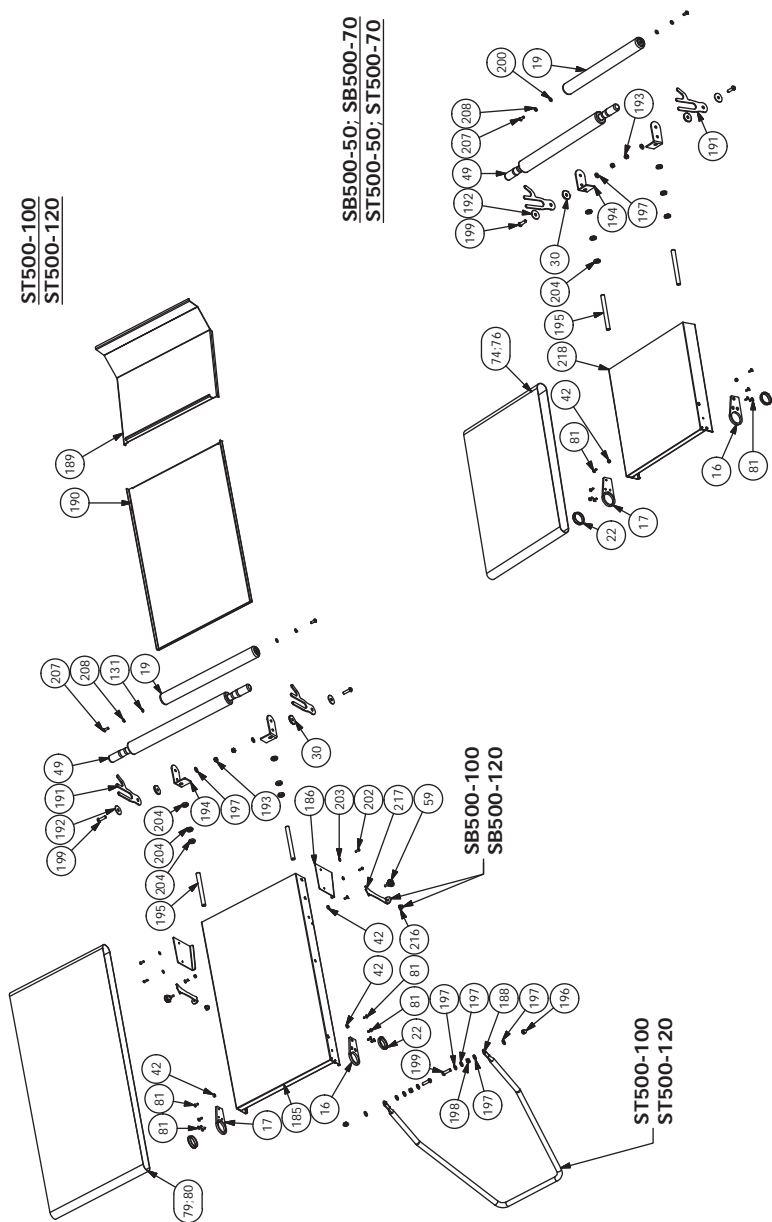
FIG. / ABB. / PИC. 21 - SB500-ST500 Parti di ricambio / Spare parts / Pieces de rechange / Repuestos / Ersatzteile / Запасные части
